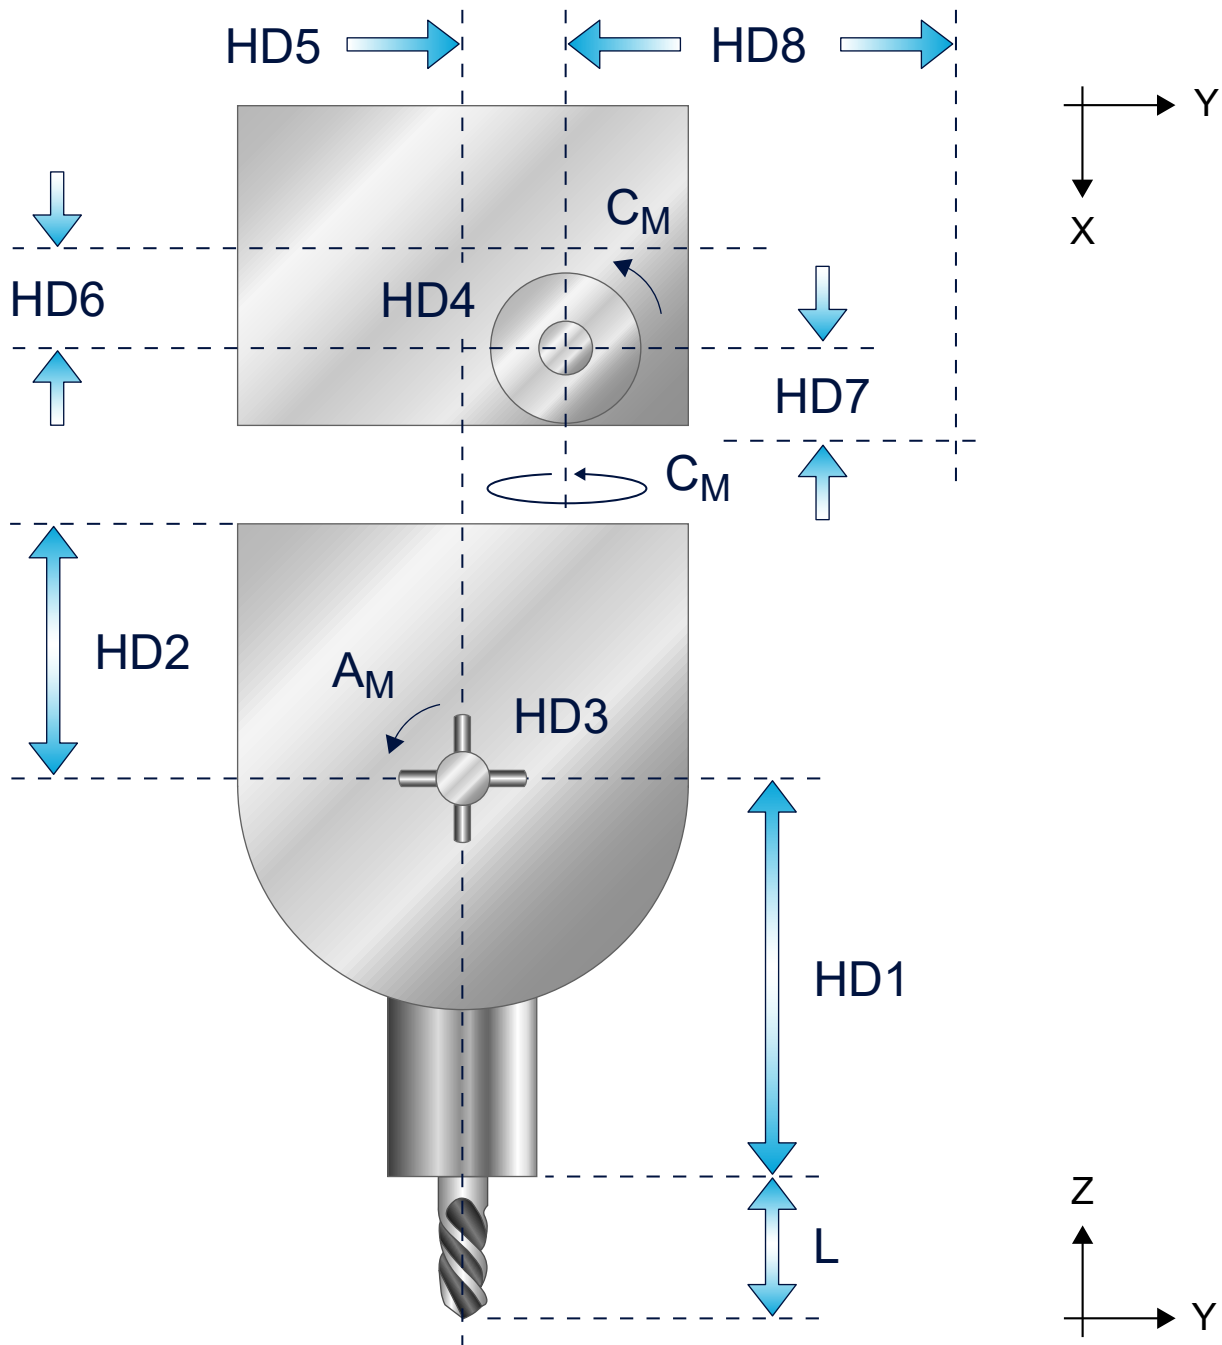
5-achsiges Bohr-/Fräswerkzeug (Ruhestellung mit $HD3=0$, $HD4=0$, $CM=0$)
